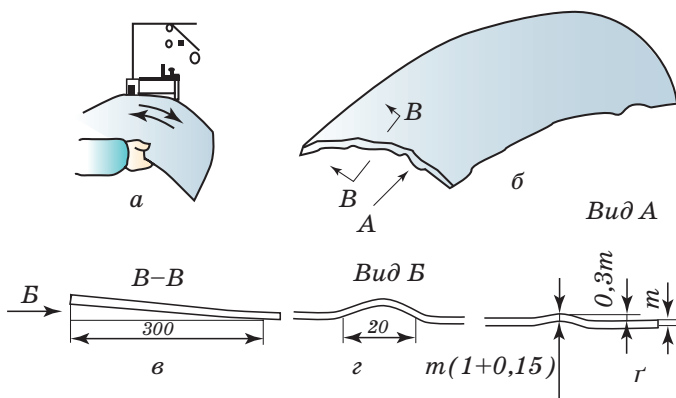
Елементи посадки, здійснюваної на посадковому верстаті: а, б — прогин заготовки; в, г — отримання гофра; г — потовщення кромки
